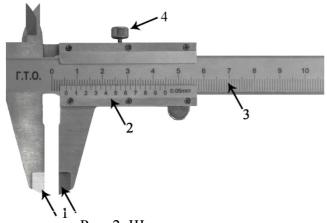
Штангенциркуль: I – губки; 2 – нониус; 3 – линейка; 4 – стопорный винт
